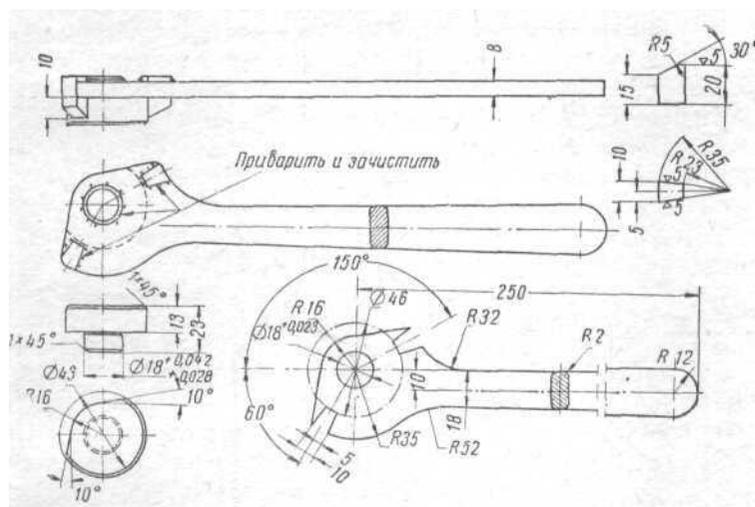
Ключ для регулировочных гаек подшипников коробки дифференциала
